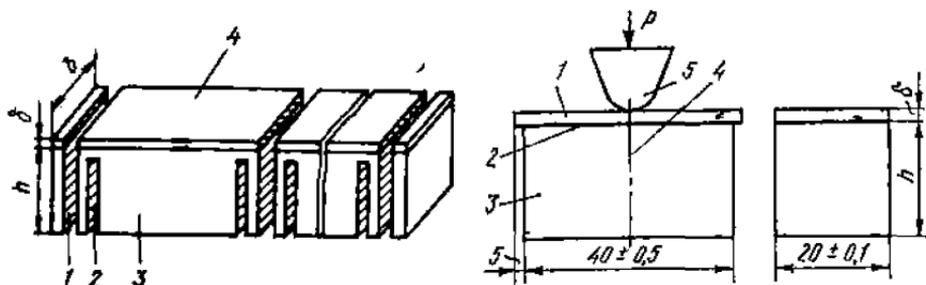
Схема выпиливания заготовки образца для испытания прочности клеевого соединения на неравномерный обрыв облицовочного материала: 1 — пропил; 2 — пропил для образования свеса; 3 — основание образца; 4 — облицовочный материал
